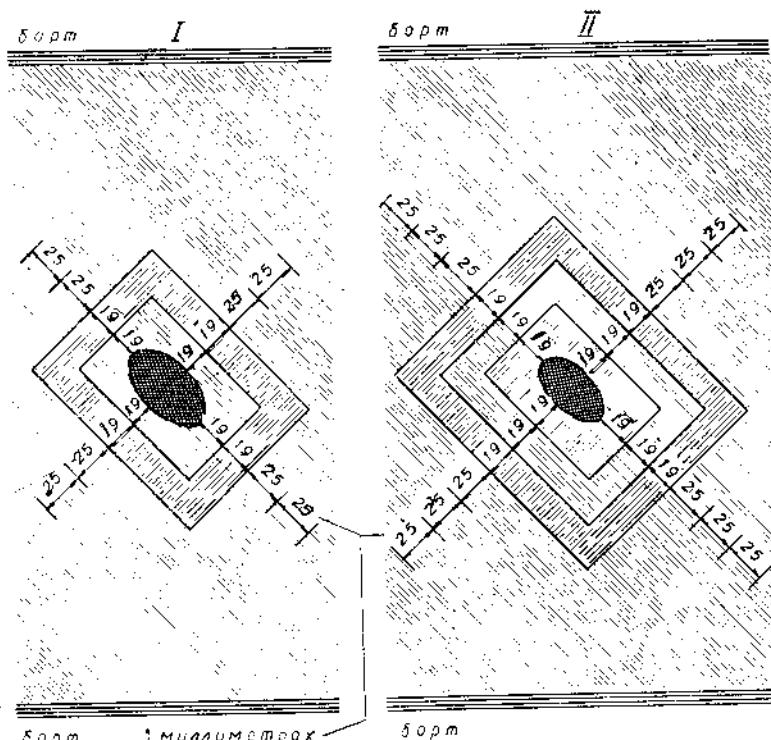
Схема накладки полосок корда при ремонте 4- и 6-слойной покрышки комбинированным способом.
